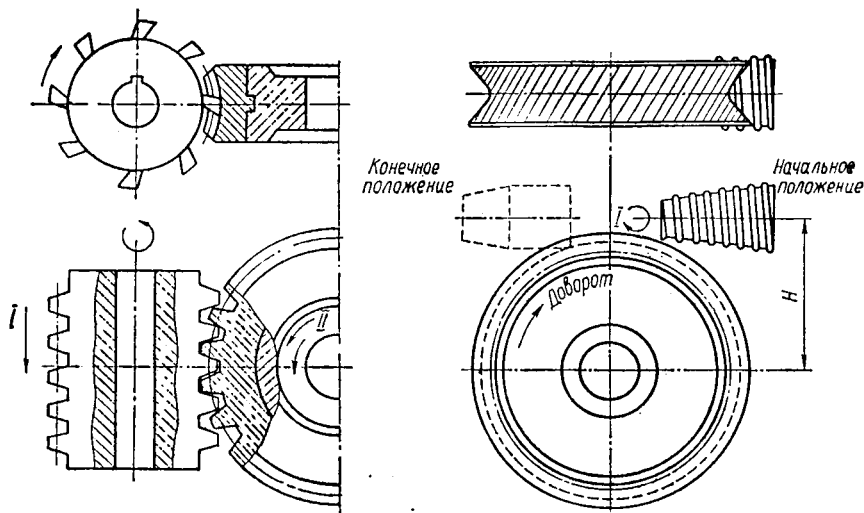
Зубонарезание червячных зубчатых колес червячными фрезами способом тангенциальной подачи
